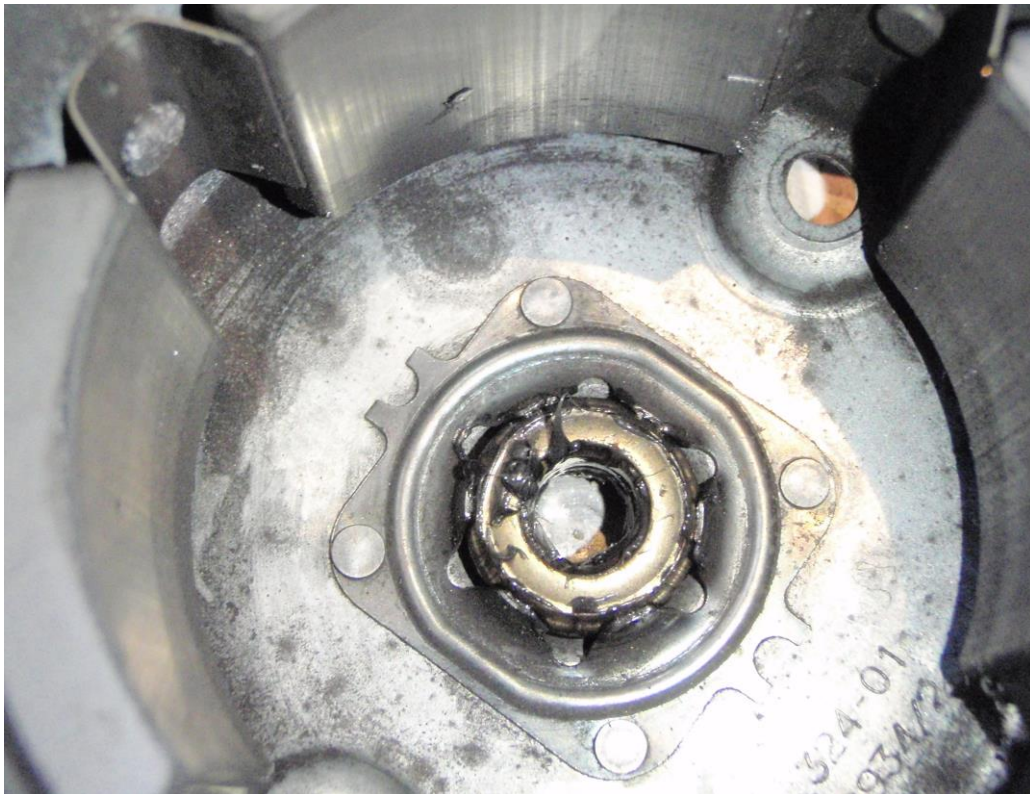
Gefettetes Lager im Gehäusedeckel
